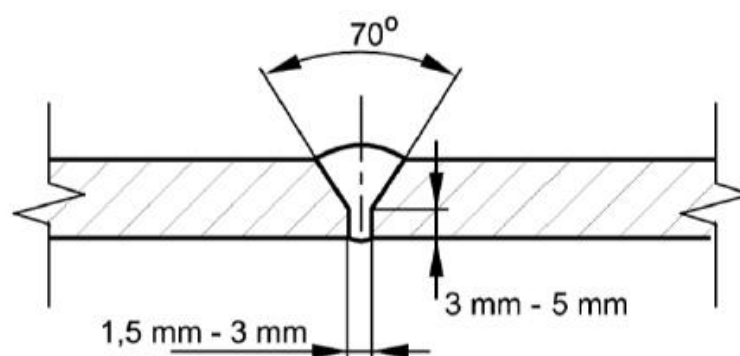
Soldadura a tope en V. UNE-EN 12493
